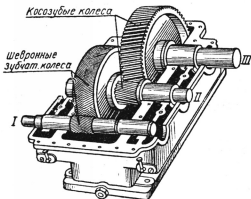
Двухступенчатый редуктор (с косозубой и шевронной парами зубчатых колес).
